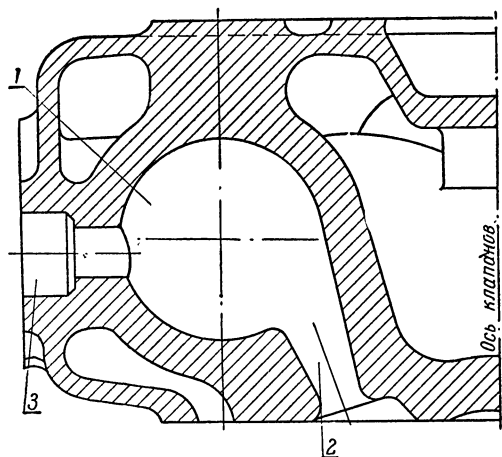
Вихревая камера головки цилиндров дизеля Д-54А:
